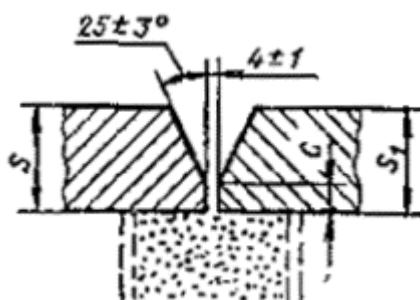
Подготовка кромок под сварку
